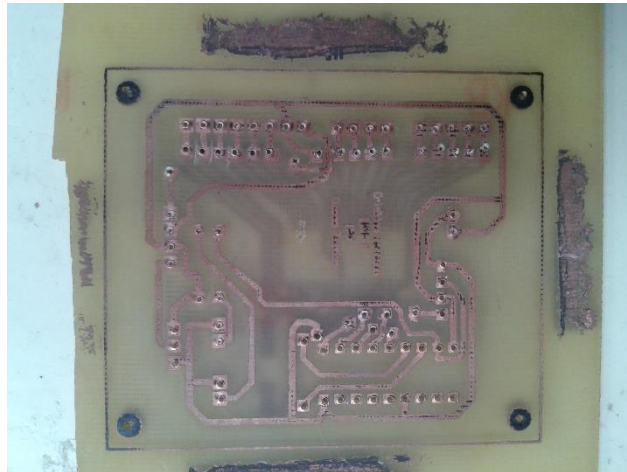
Baquelita módulo Cuerpo Técnico bottom
